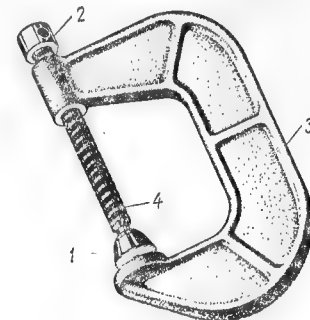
1 — бабка винта; 2 — головка винта; 3 — скоба; 4 — винт
